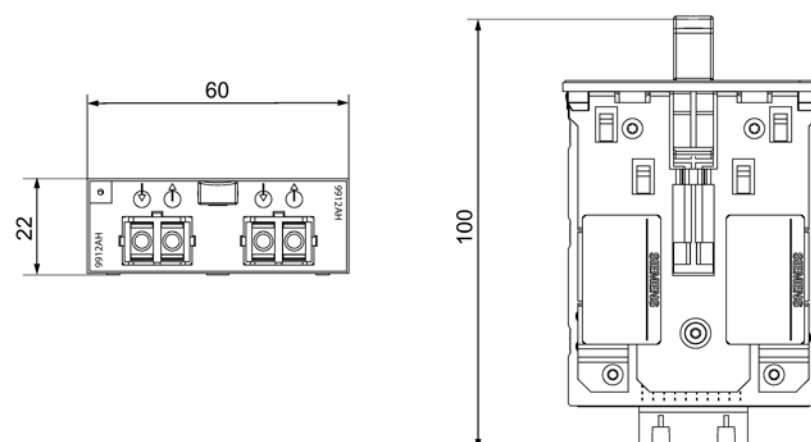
MM900 Dessin coté 7 : Ports optiques RJ SC
